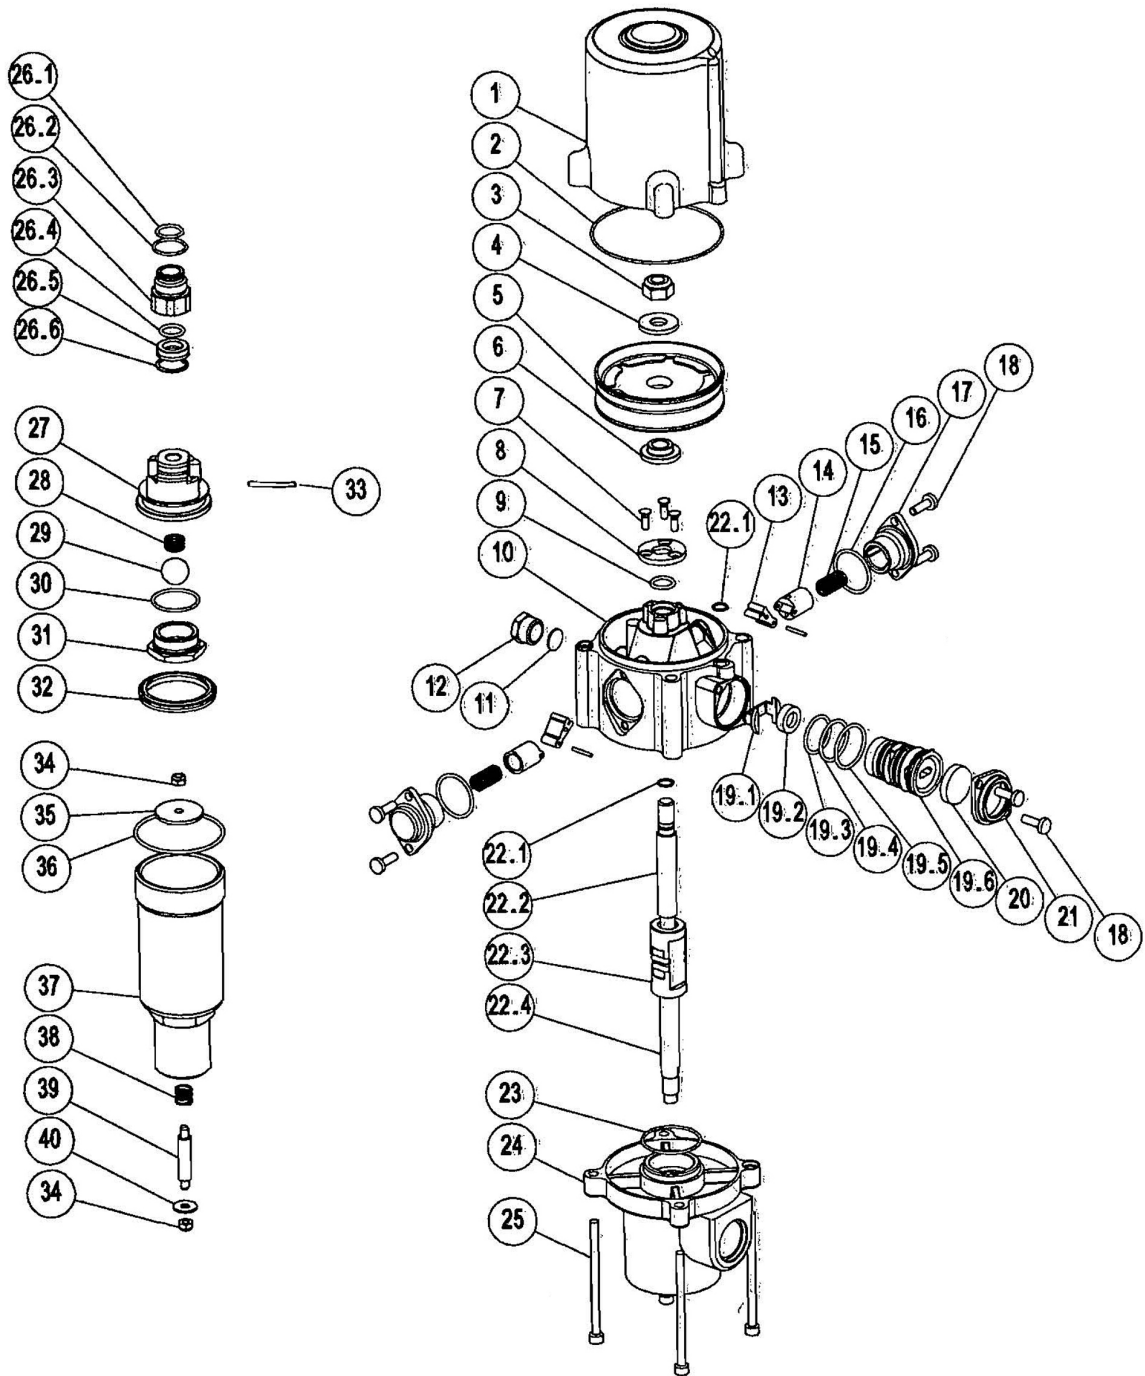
Explosionsdarstellung der Pneumatik-Ölpumpe
